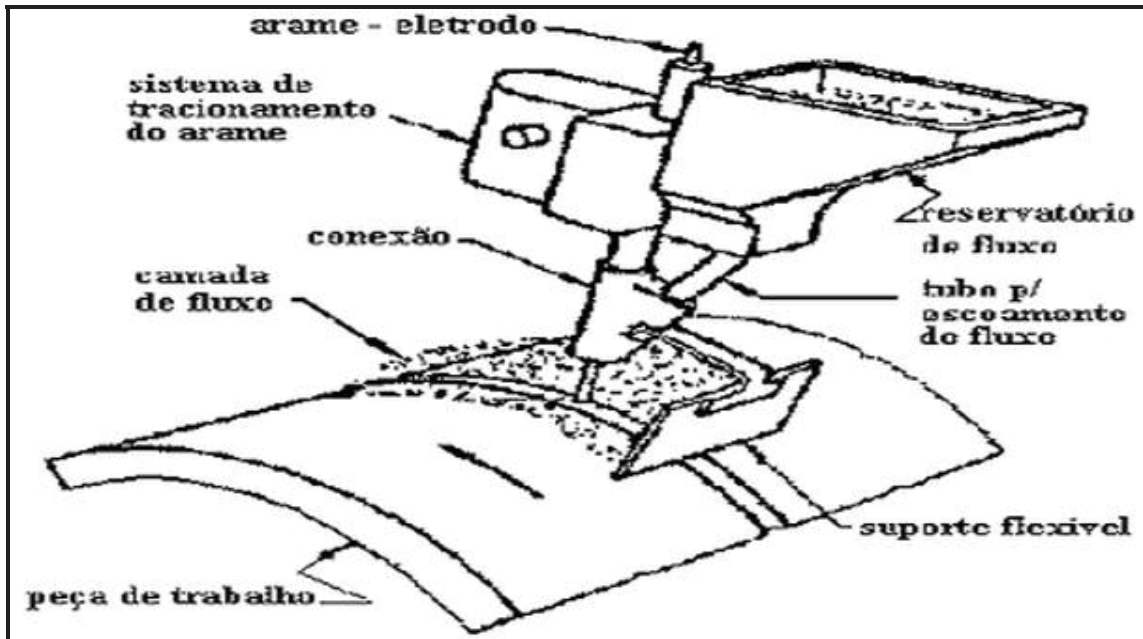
Soldagem por Arco Submerso (internet: AMIGONERD; acessado em Outubro de 2012).
